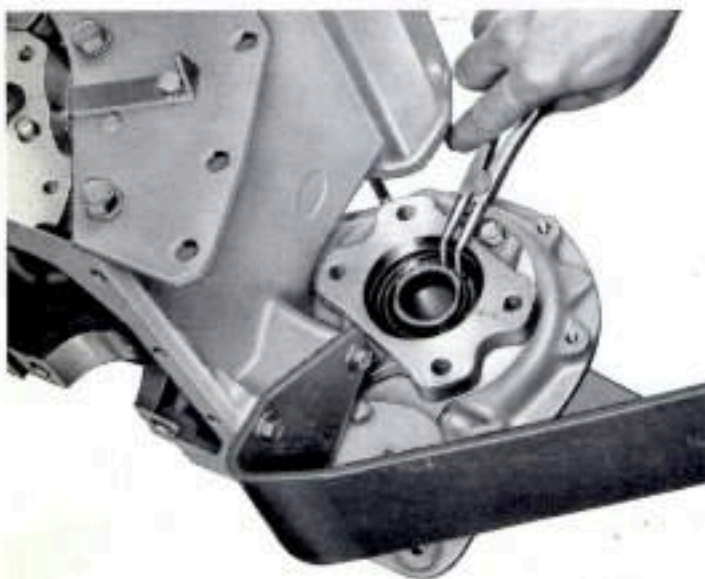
Smontaggio del motore: viene tolto l'anello elastico di ritegno ingranaggio comando pompa iniezione.
